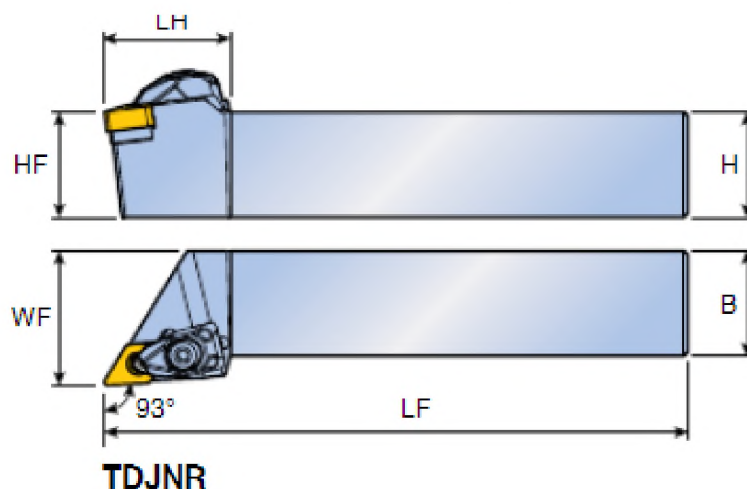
Державка TDJNR 2525 M15 [1, с. A113]:
